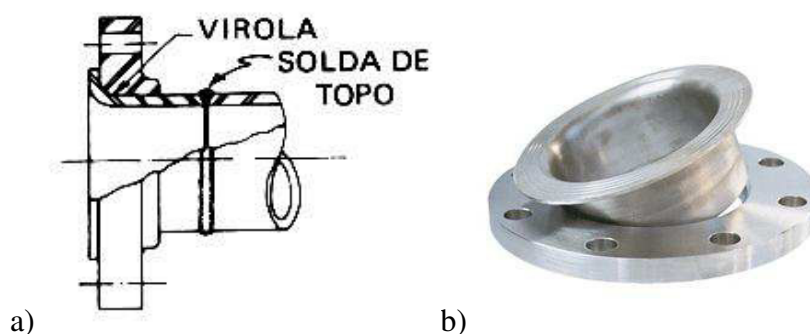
a) Desenho Representativo de um Flange Solto (SENAI, 1997). b) Flange Solto (AHAD Tubeline co., 2012)
